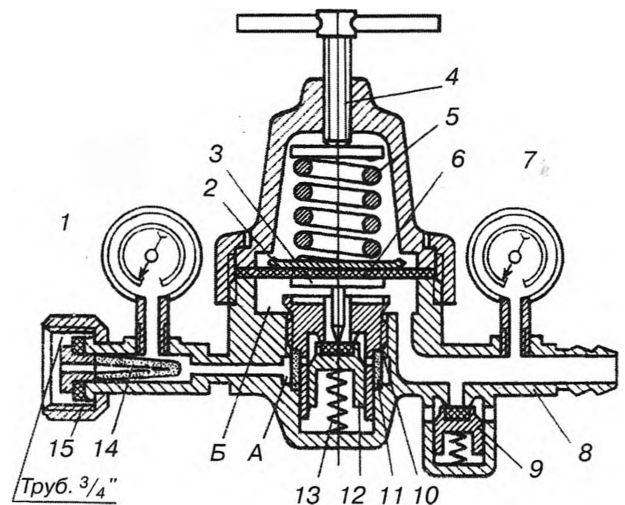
Одноступінчастий кисневий редуктор: 1, 7 — манометри; 2 — натискний диск; 3 — штовхач; 4 — регулювальний гвинт; 5 — натискна пружина; 6 — мембрана; 8 — ніпель; 9 — запобіжний клапан; 10 — сідро; 11, 14 — фільтри; 12 — редуруючий клапан; 13 — пружина; 15 — накидна гайка; А — камера високого тиску; Б — робоча камера
